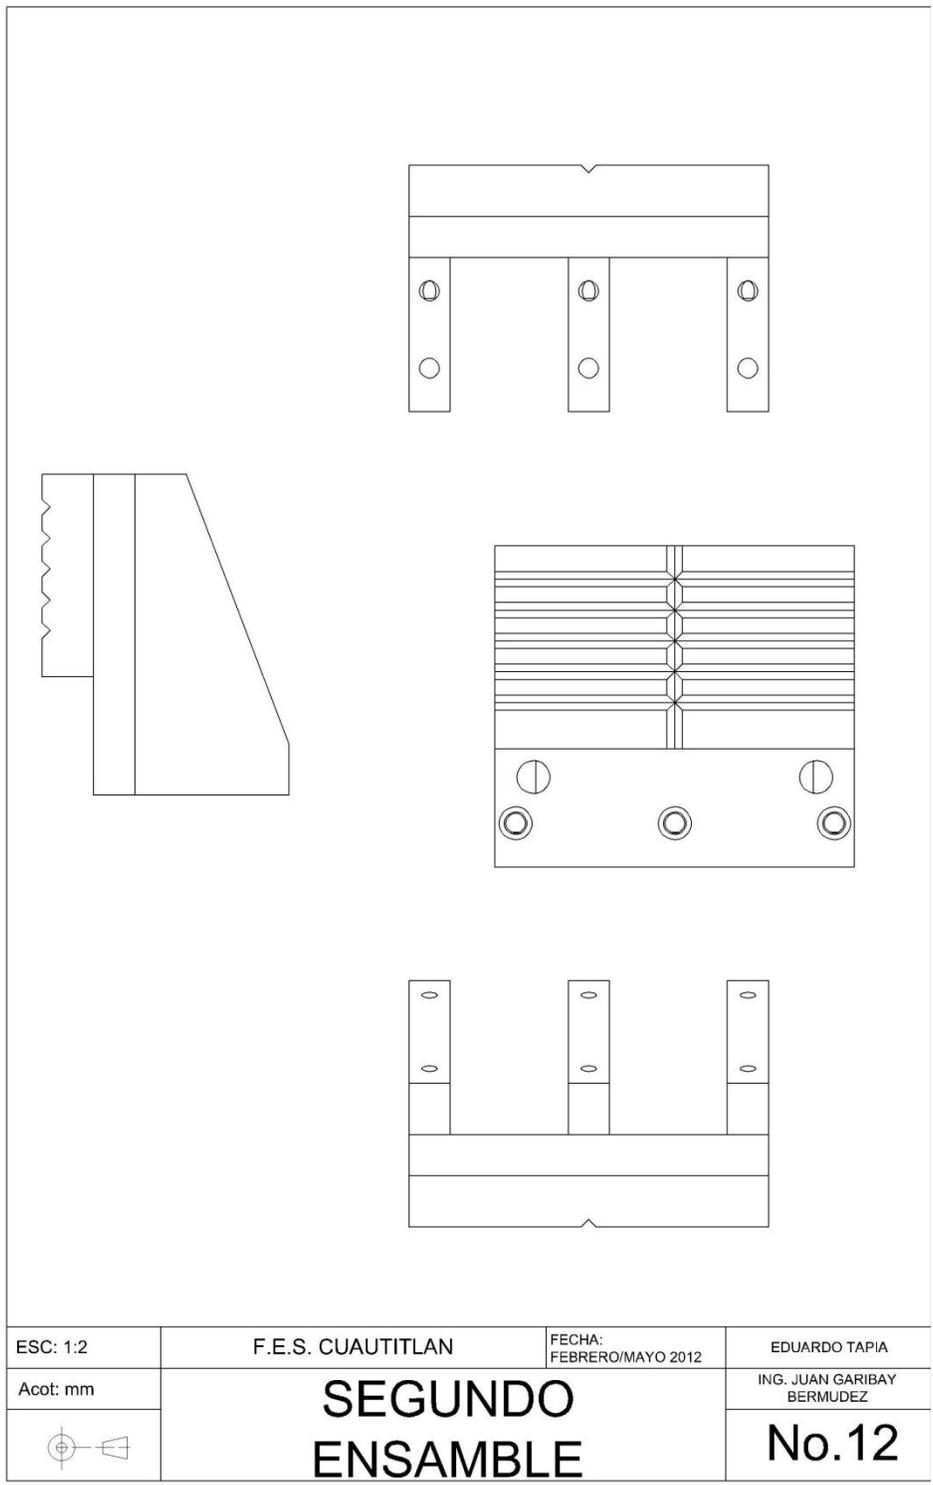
Ilustración del ensamble requerido para la construcción de los cabezales fijos.
